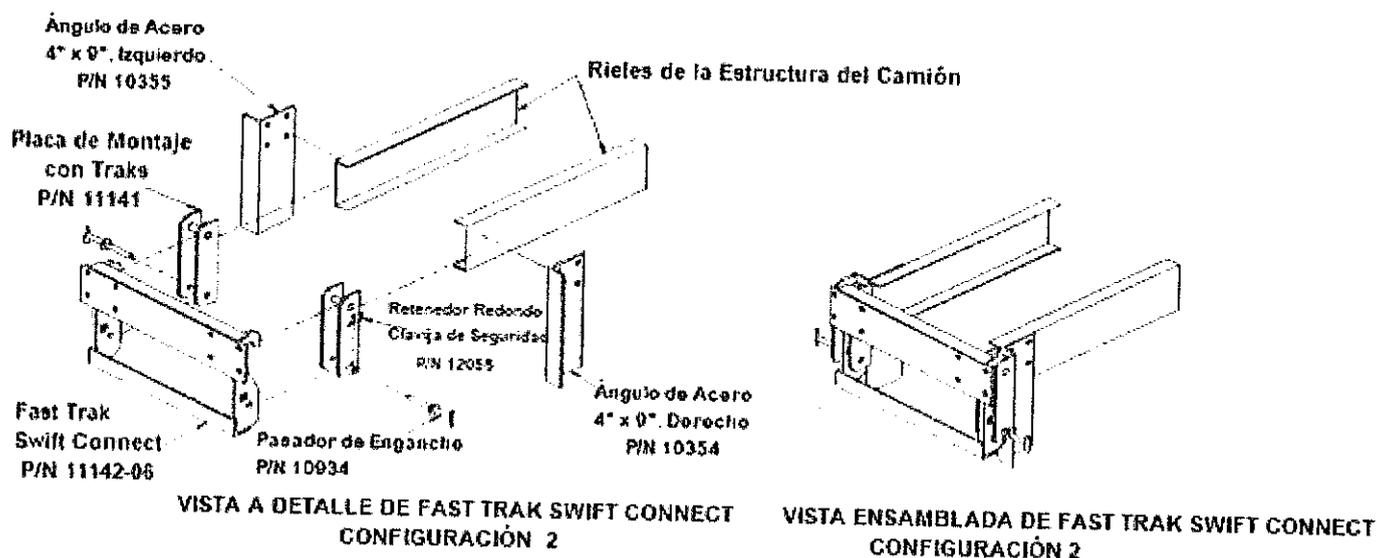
Vista a detalle y ensamblada de la Configuración 2.
